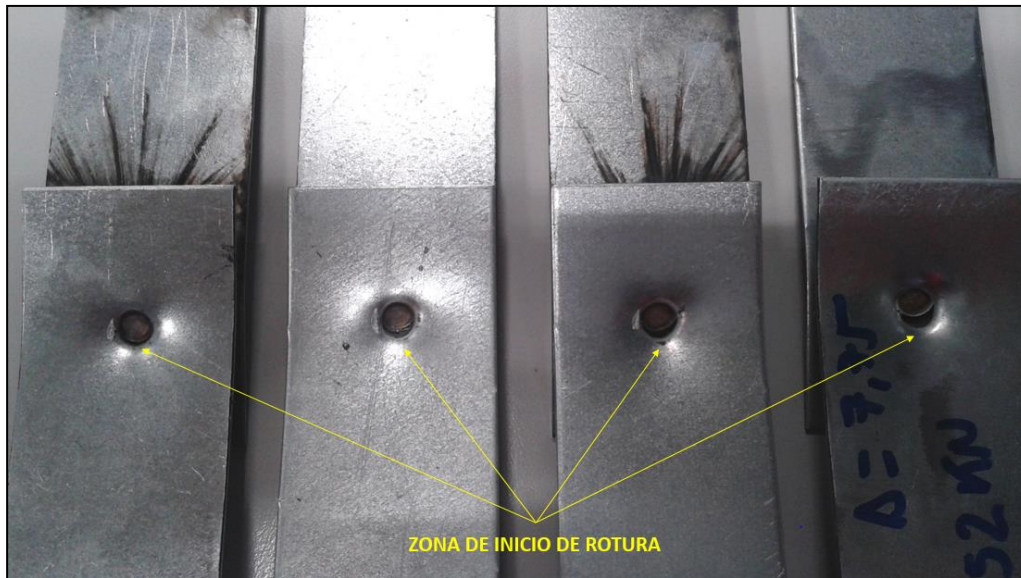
Vista general de una probeta con rotura tipo III, con vista en detalle del punto de soldadura.
